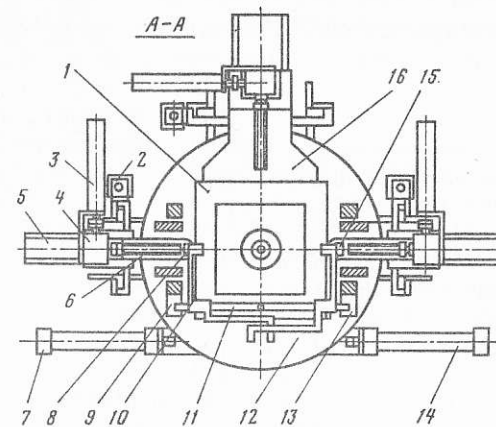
Устройство для автоматического базирования и закрепления заготовок
